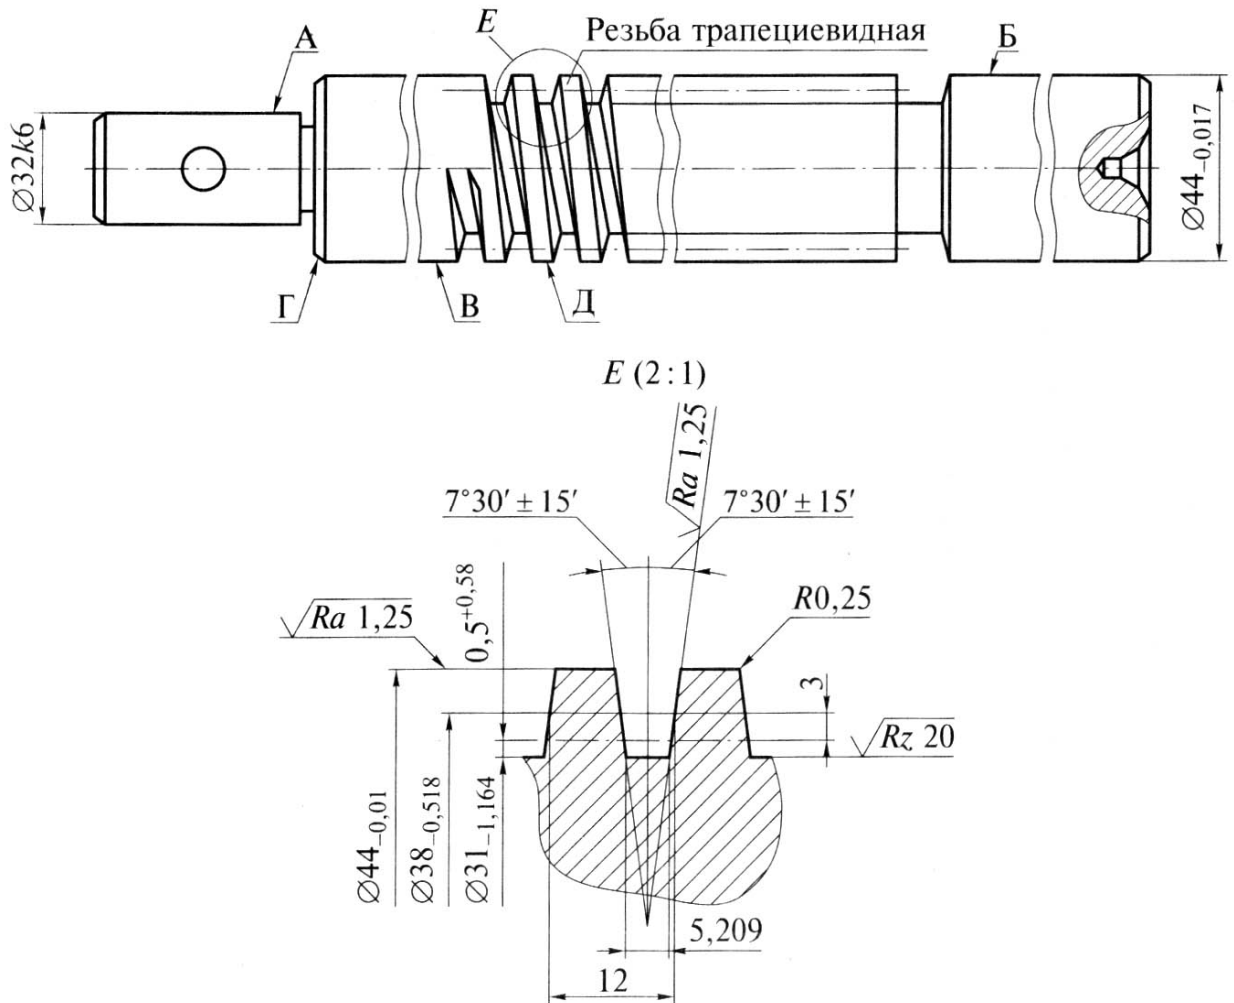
Креслення ходового гвинта металорізального верстата з деякими вимогами по формі, розташуванню і шорсткості поверхонь.
